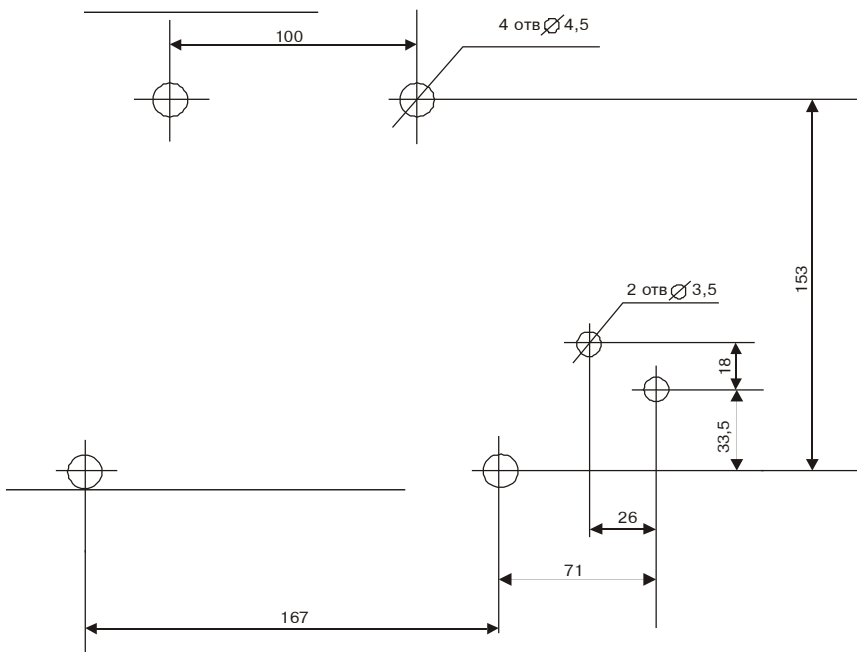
Схема разметки для установки БЦ-А исполнение 2
